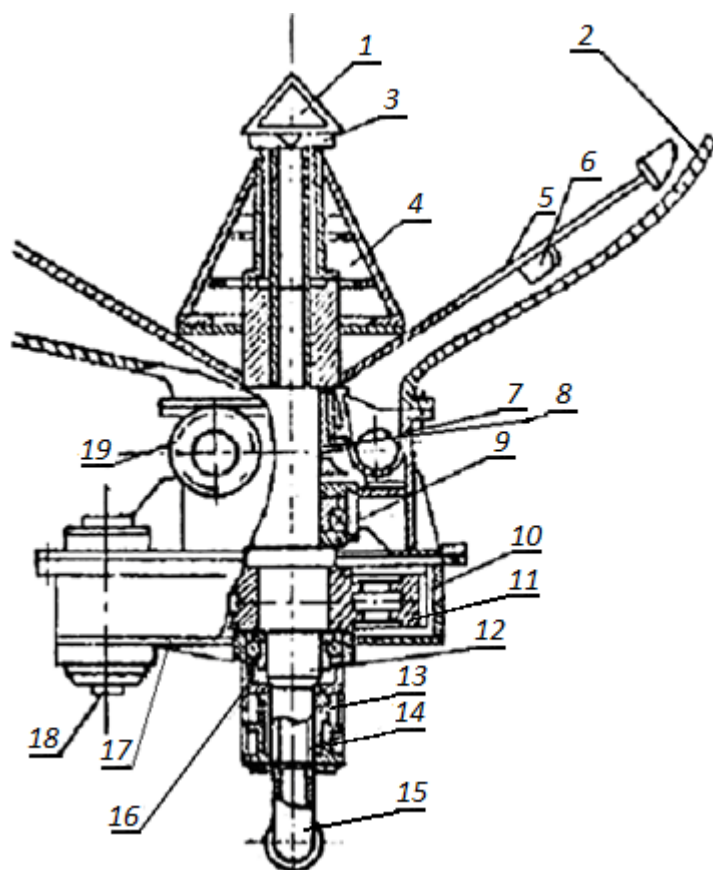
Разгрузочное устройство варочного котла установки непрерывной варки целлюлозы:
